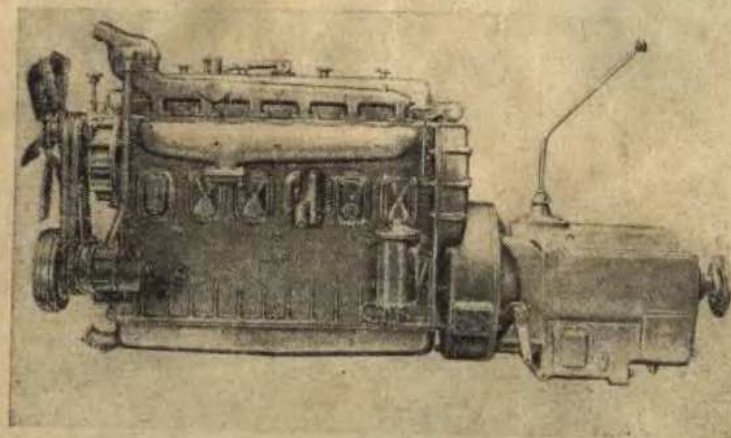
Общий вид двигателя ЯАЗ-М204А:
